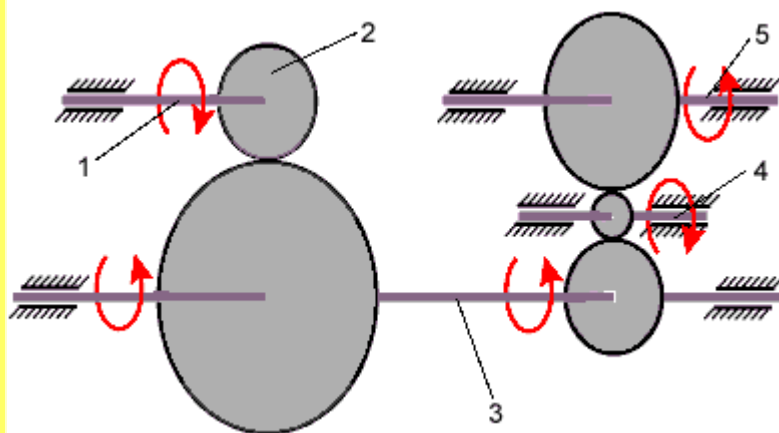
Схема передачи крутящего момента при включении задней передачи 1 - первичный вал; 2 - шестерня первичного вала; 3 - промежуточный вал; 4 - шестерня и вал передачи заднего хода; 5 - вторичный вал
